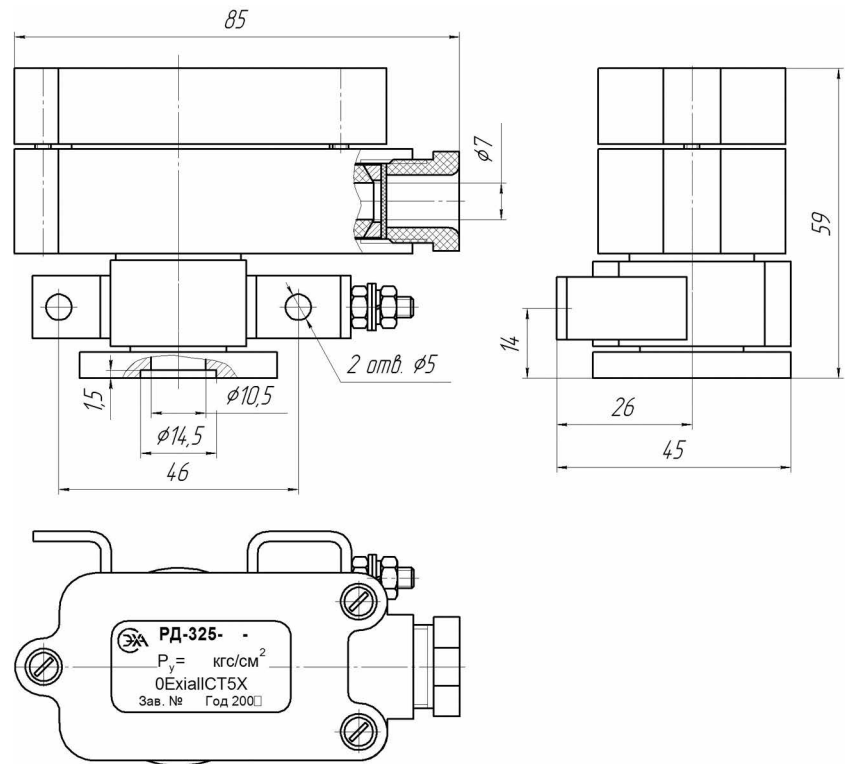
Габаритные и установочные размеры реле давления РД-325
